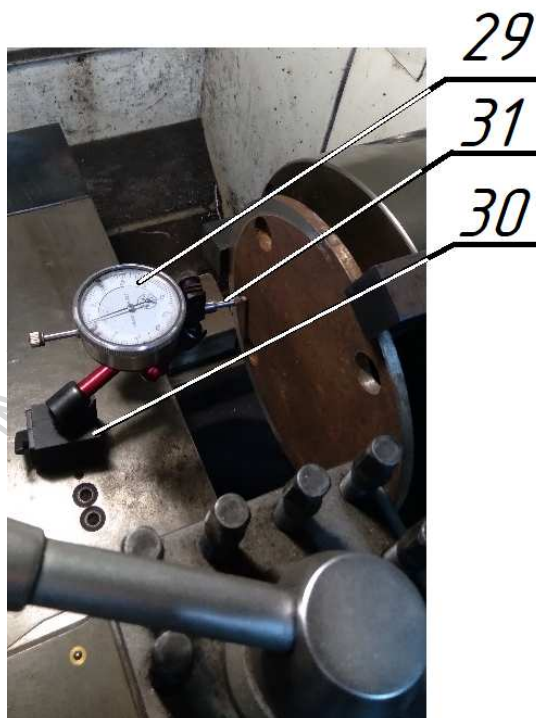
Проверка биения правой торцевой поверхности заготовки «Диск».
